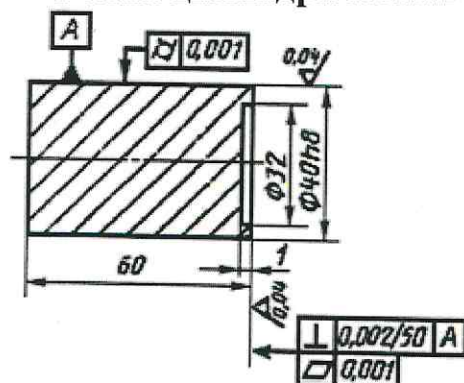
Чертеж общего вида ролика цилиндрического
